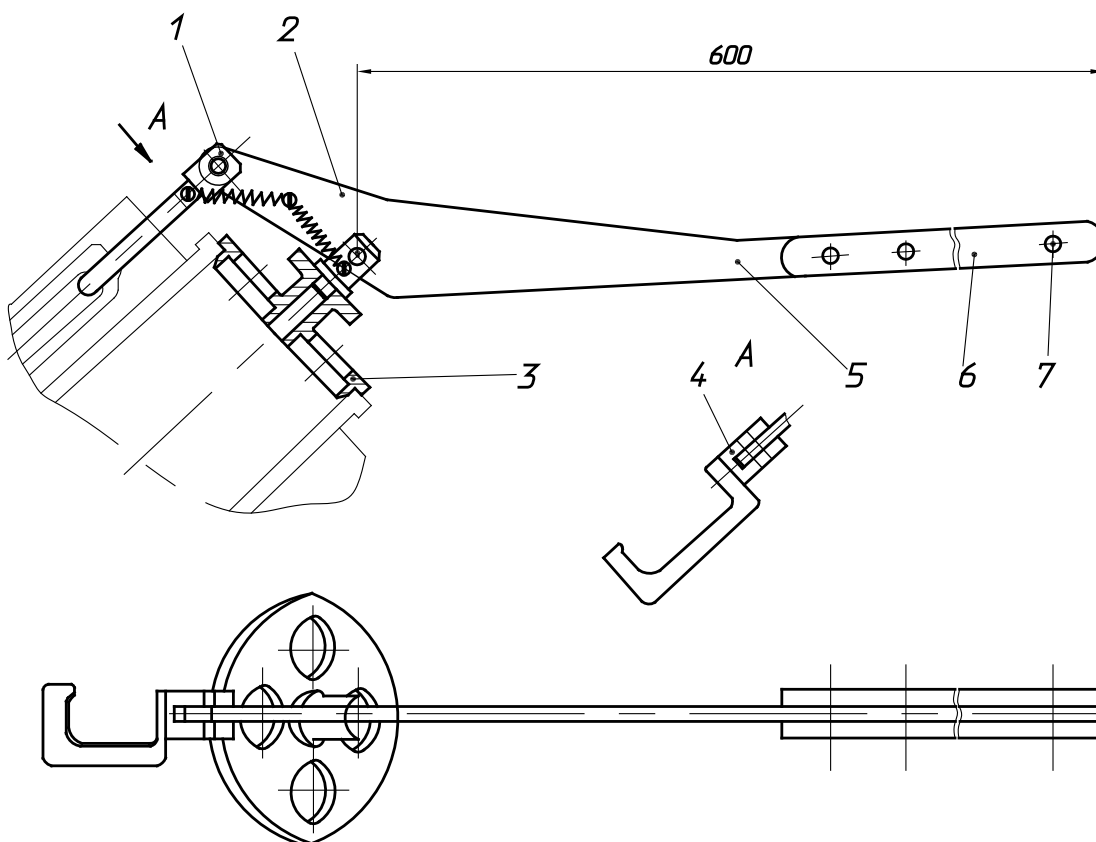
Приспособление для запрессовки гильз в цилиндр
